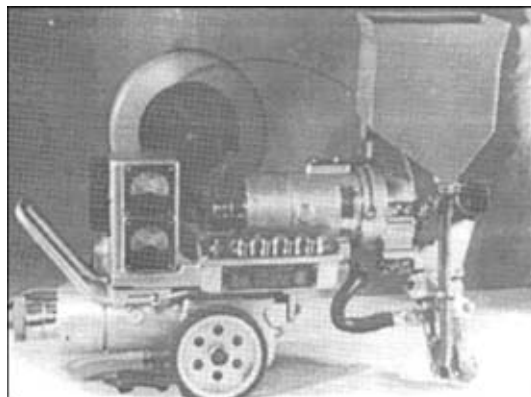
Автомат АСУ-138 для сварки под флюсом наклонным электродом тавровых соединений судовых конструкций
